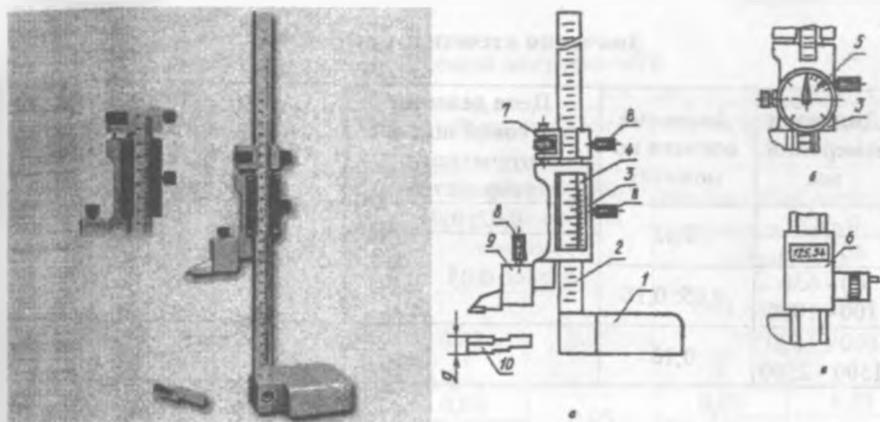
24. Штангенрейсмас: а) - общий вид, б) – устройство:
